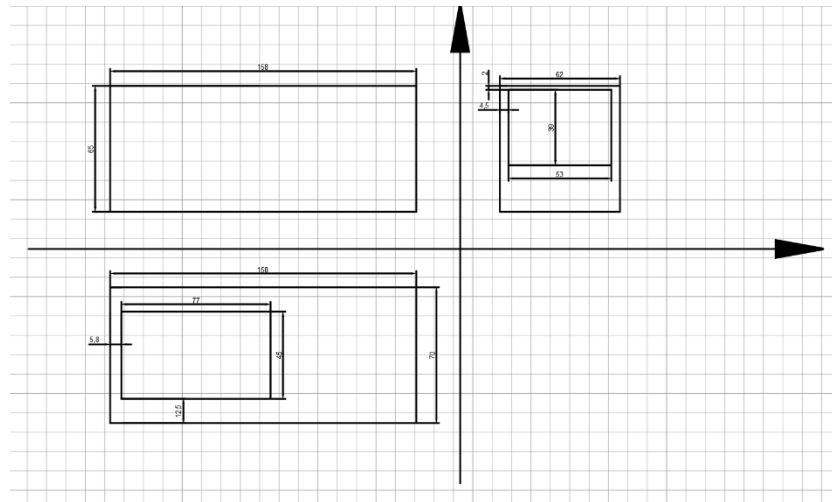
Кресленик корпусу повербанка в трьох проекціях
